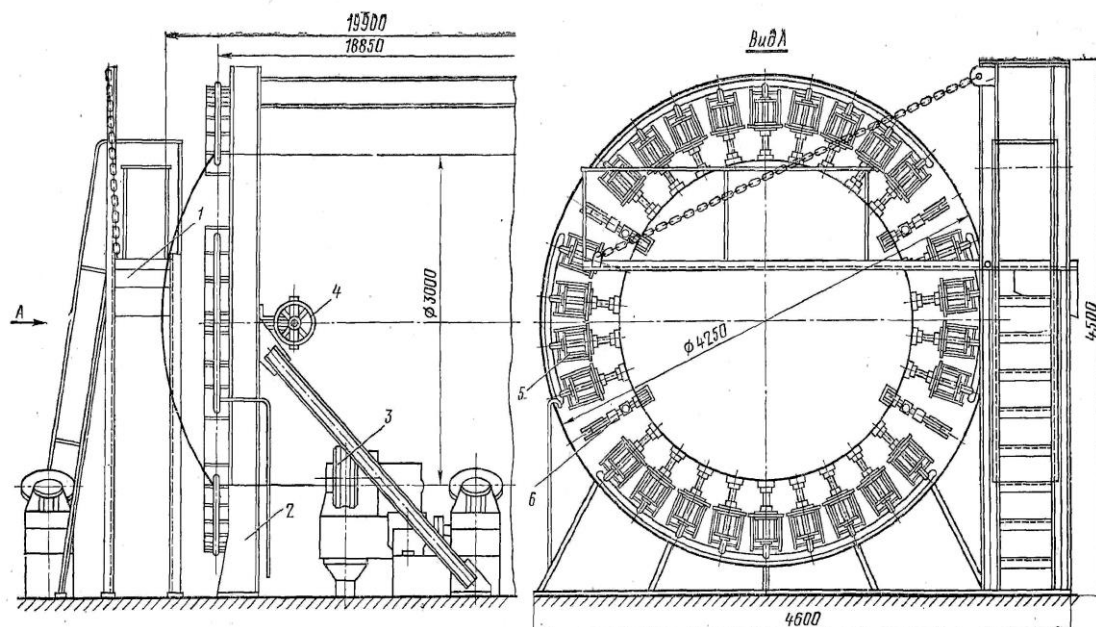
Стенд для приварки днищ к обечайке котла цистерны:
